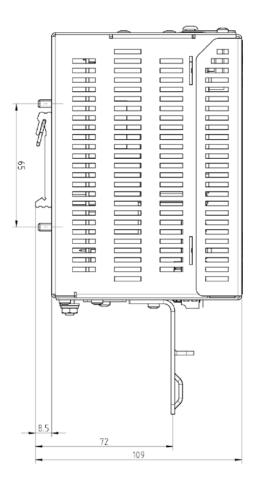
Esquema acotado de IE Switch X302-7EEC - Vista lateral
